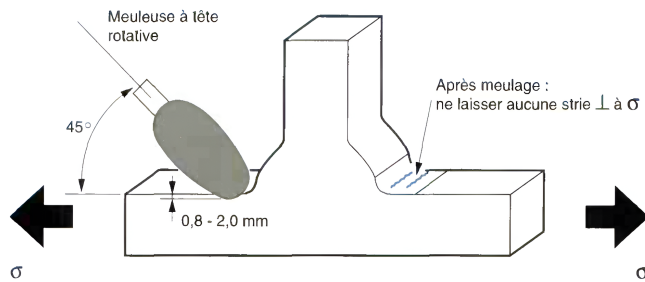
Meulage d'une soudure [26].
